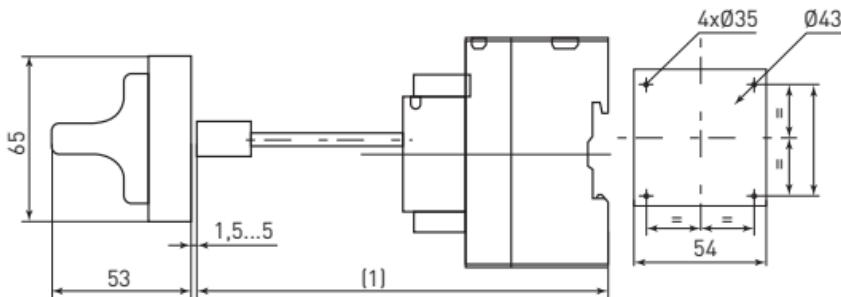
Габаритные размеры черной выносной рукоятки GV2
